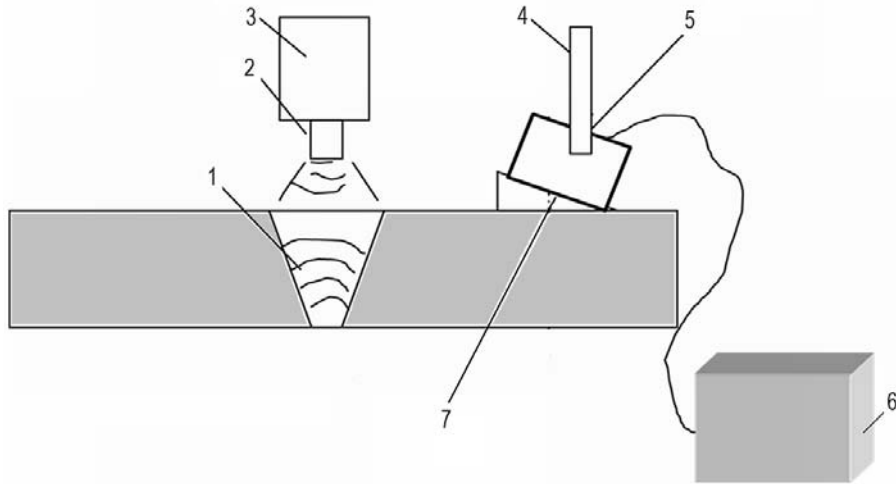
Схема воздействия ультразвука на сварное соединение в процессе сварки: 1 – сварное соединение; 2 – электрод; 3 – держатель; 4 – кронштейн; 5 – ультразвуковой преобразователь; 6 – ультразвуковой генератор; 7 – призма
